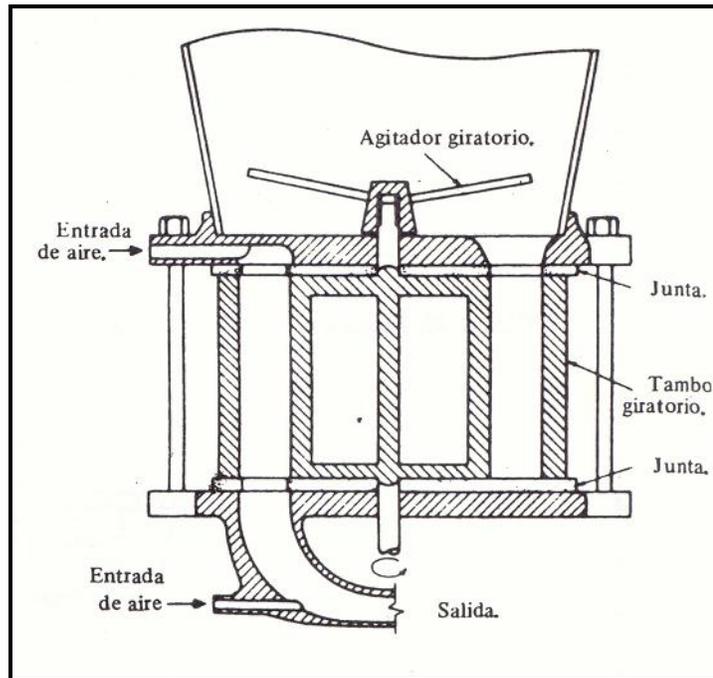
Lanzadora de tambor giratorio (detalle del tambor).
